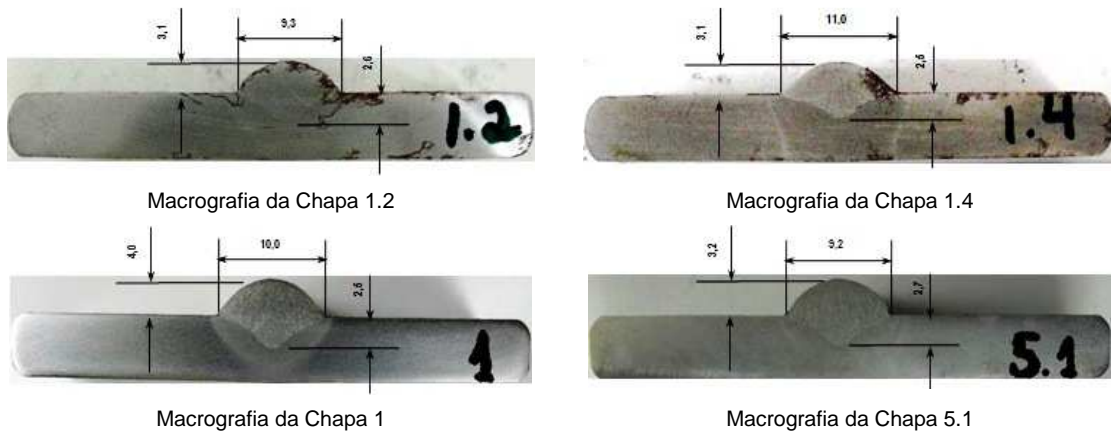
Macrografias com altura do reforço (r), largura do cordão de solda (b) e a penetração das soldas com $Ar+10\%CO_2$.
